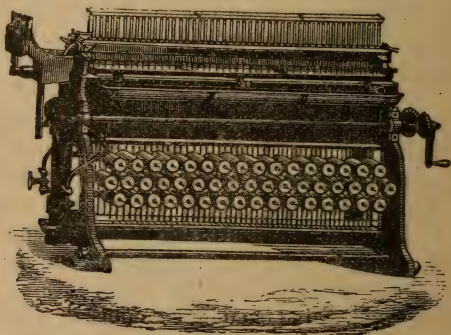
Machine à mouler les bougies (Morane aîné).
